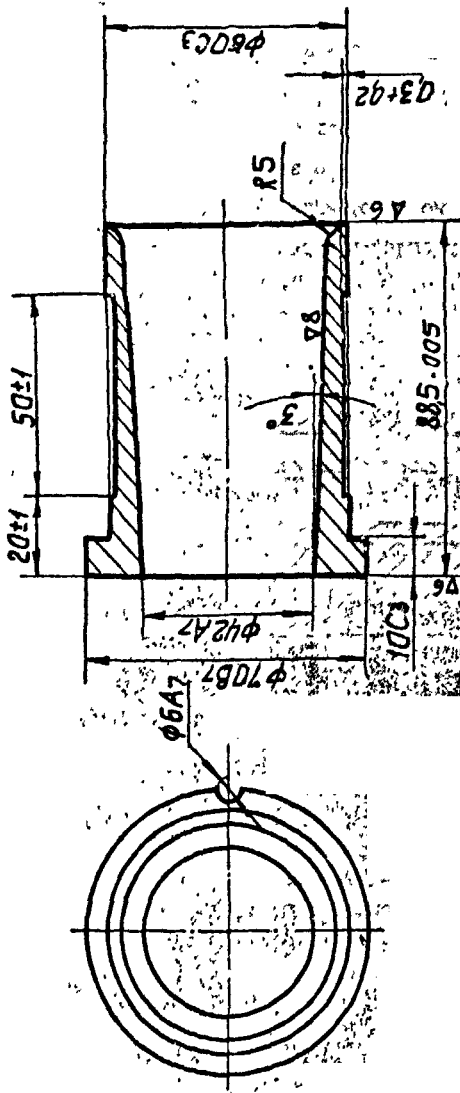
II. Конструкция и класс точности посадочных размеров
